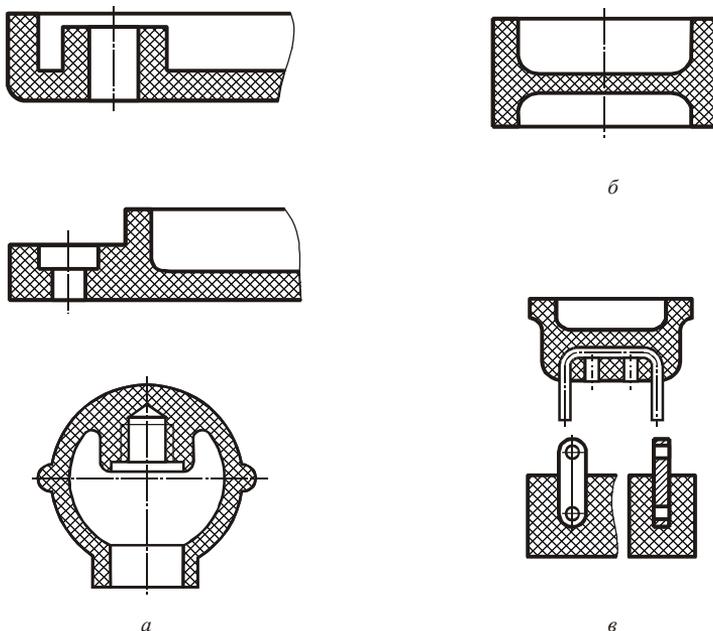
Примеры деталей, изготовленных из пластмасс:
